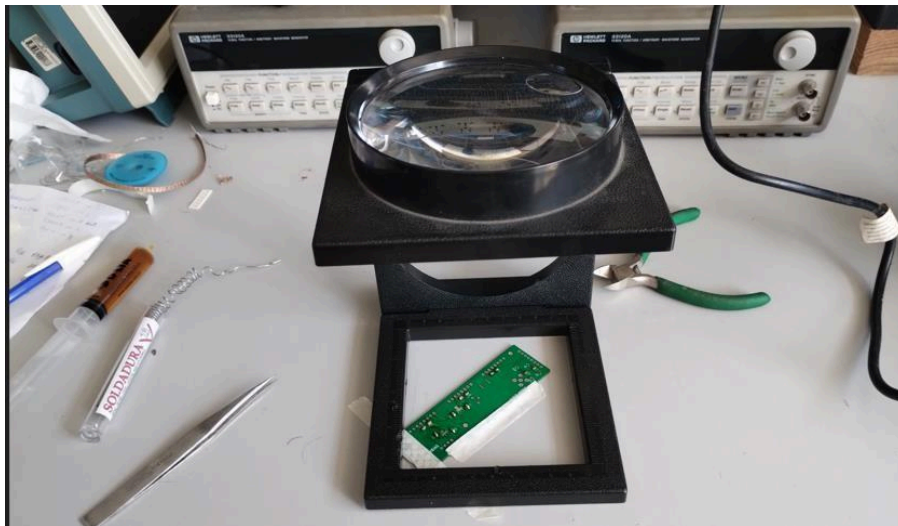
Montaje y soldado de la placa acondicionamiento de señal.
